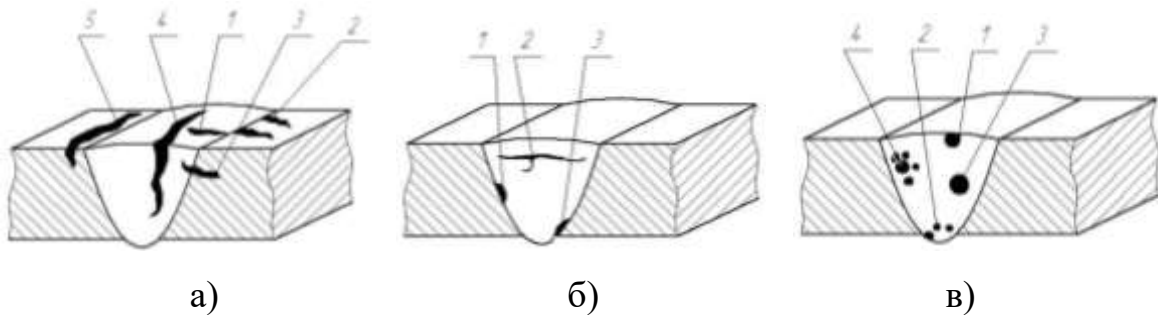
Дефекти зварних швів сталі 15ХСНД
